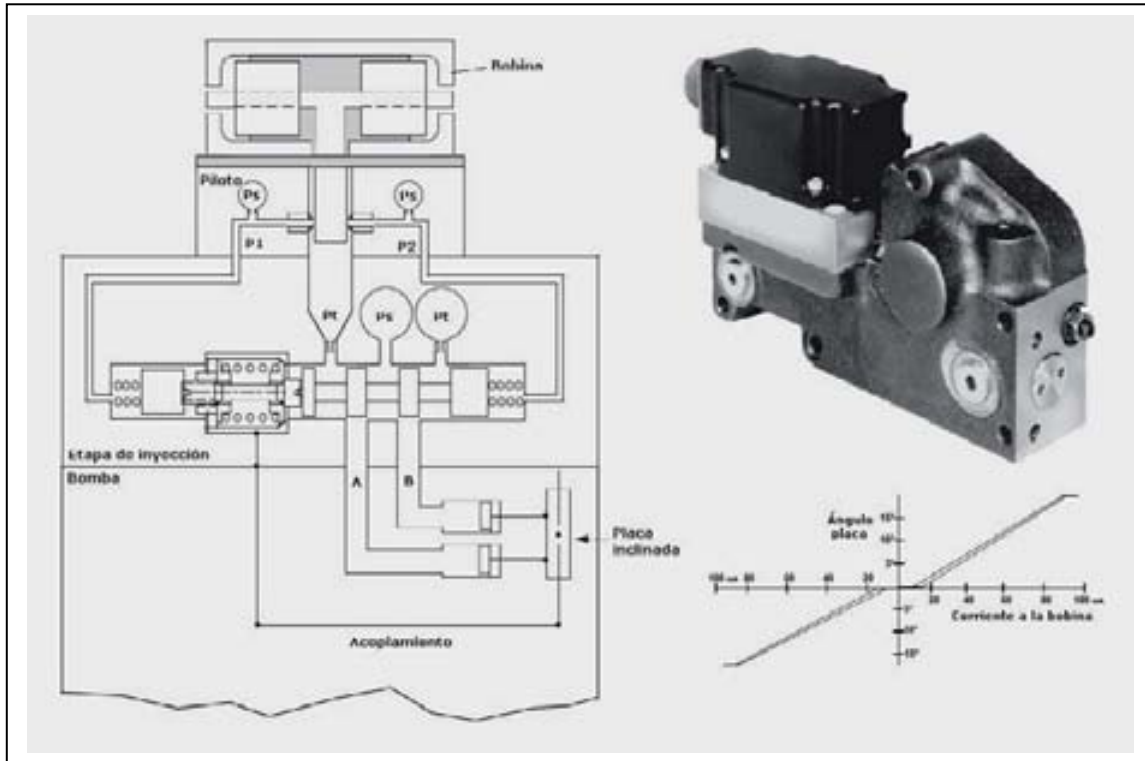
Detalle del mando de la placa inclinada en una bomba axial. Fuente: Sauer Danfoss
